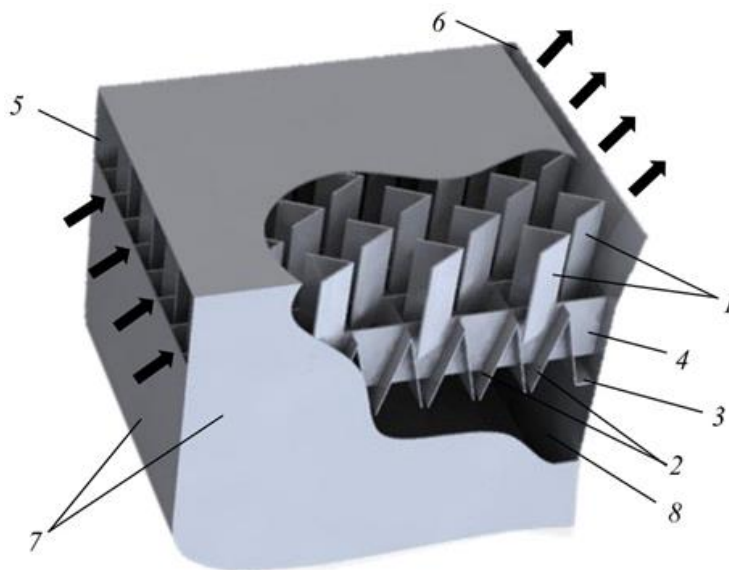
Сепаратор с V-образными конструктивными элементами (вид с многоступенчатым разрезом):
